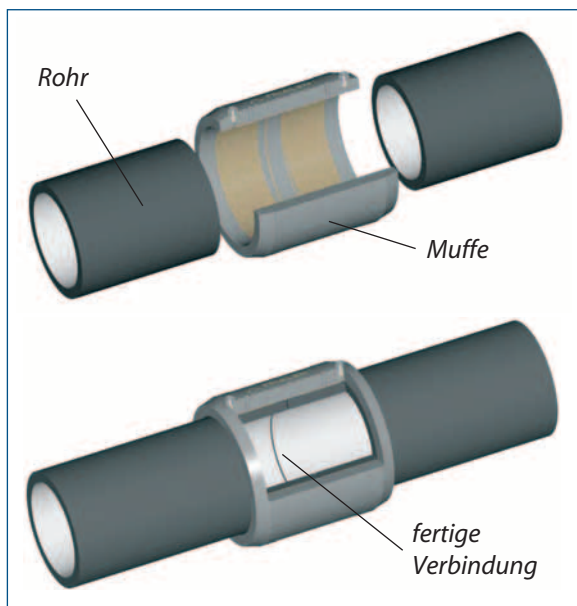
■ Prinzip der Heizwendelschweißtechnik
